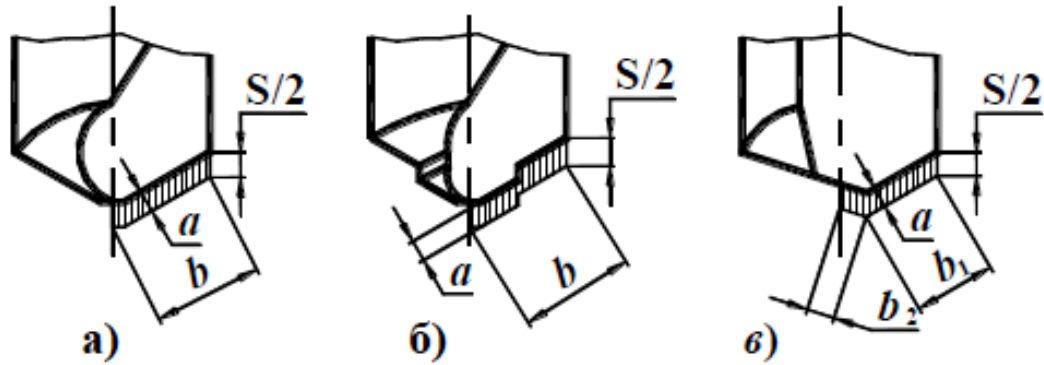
Схеми шару, що зрізається при свердлінні отворів в залежності від форми заточування вершини різальної частини інструменту: а) стандартне свердло; б) стандартне свердло з елементами дроблення стружки; в) свердло однокромкове.
